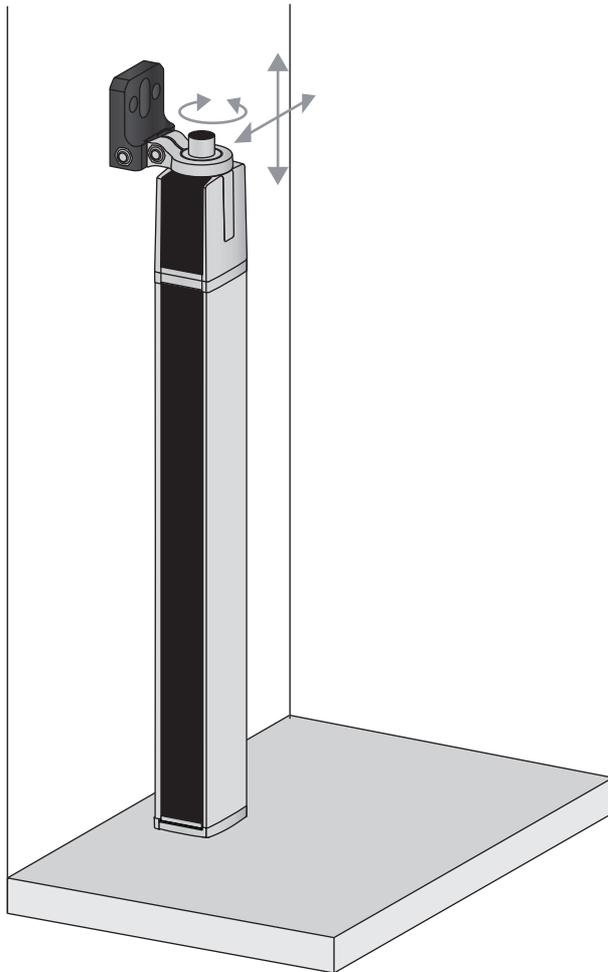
Befestigung direkt auf dem Maschinentisch
